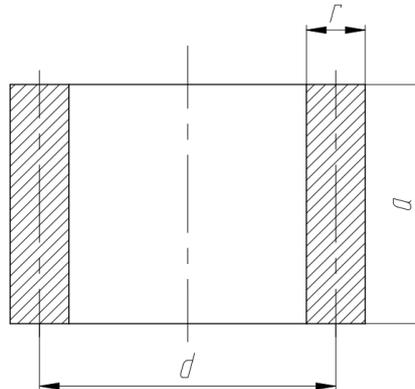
Разрез круговой катушки прямоугольного поперечного сечения
